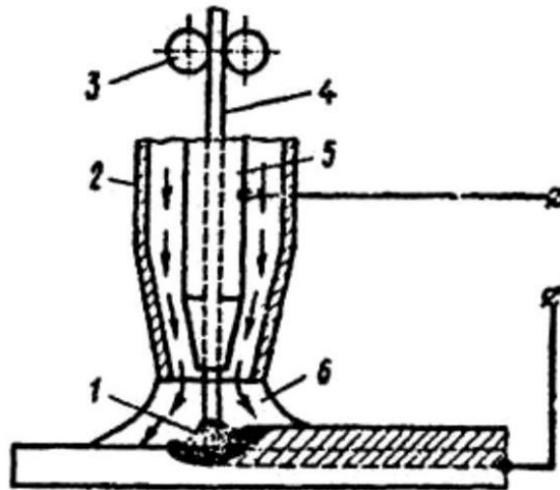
Схема механізованого зварювання суцільним дротом в середовищі інертного газу
